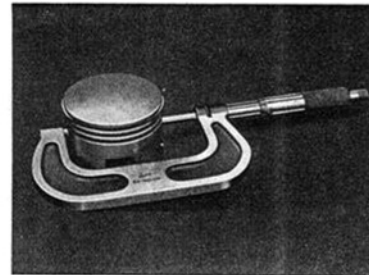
Messen des Kolbens zwischen Bolzenbohrung und unterer Ringnute mittels Mikrometers Nr. 0998
